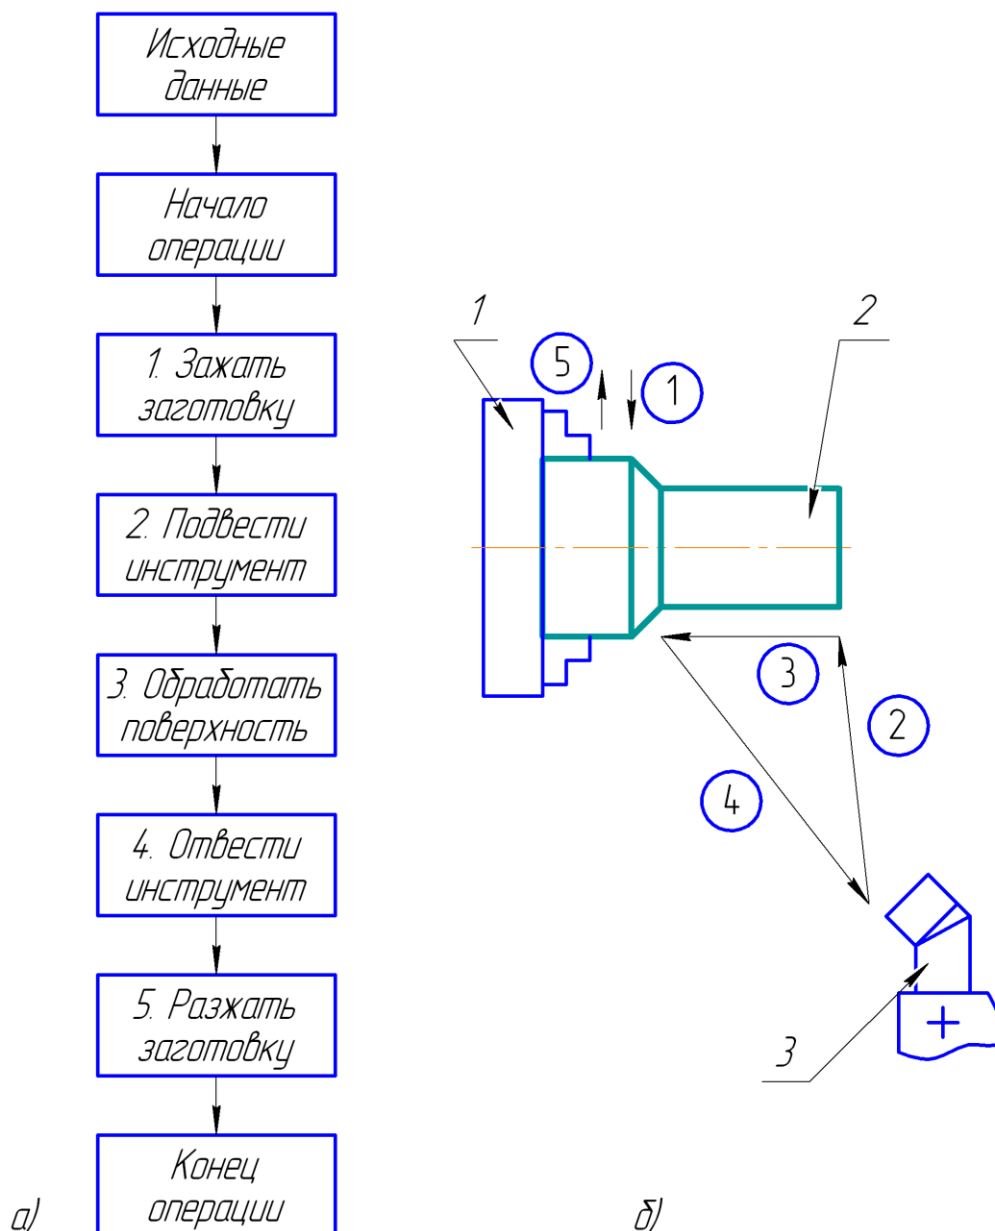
Линейный алгоритм. а) блок-схема; б) эскиз токарной операции: 1 – зажимное приспособление; 2 – ступенчатый вал; 3 – инструмент.
